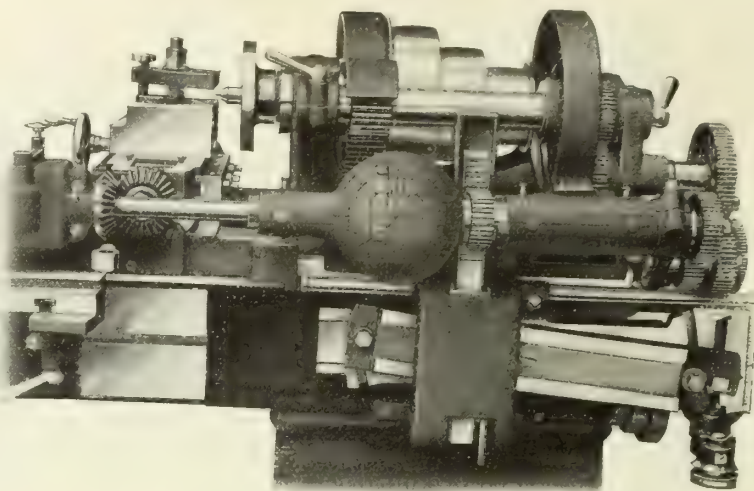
Hinterdrehbank (Teil-Rückansicht)
